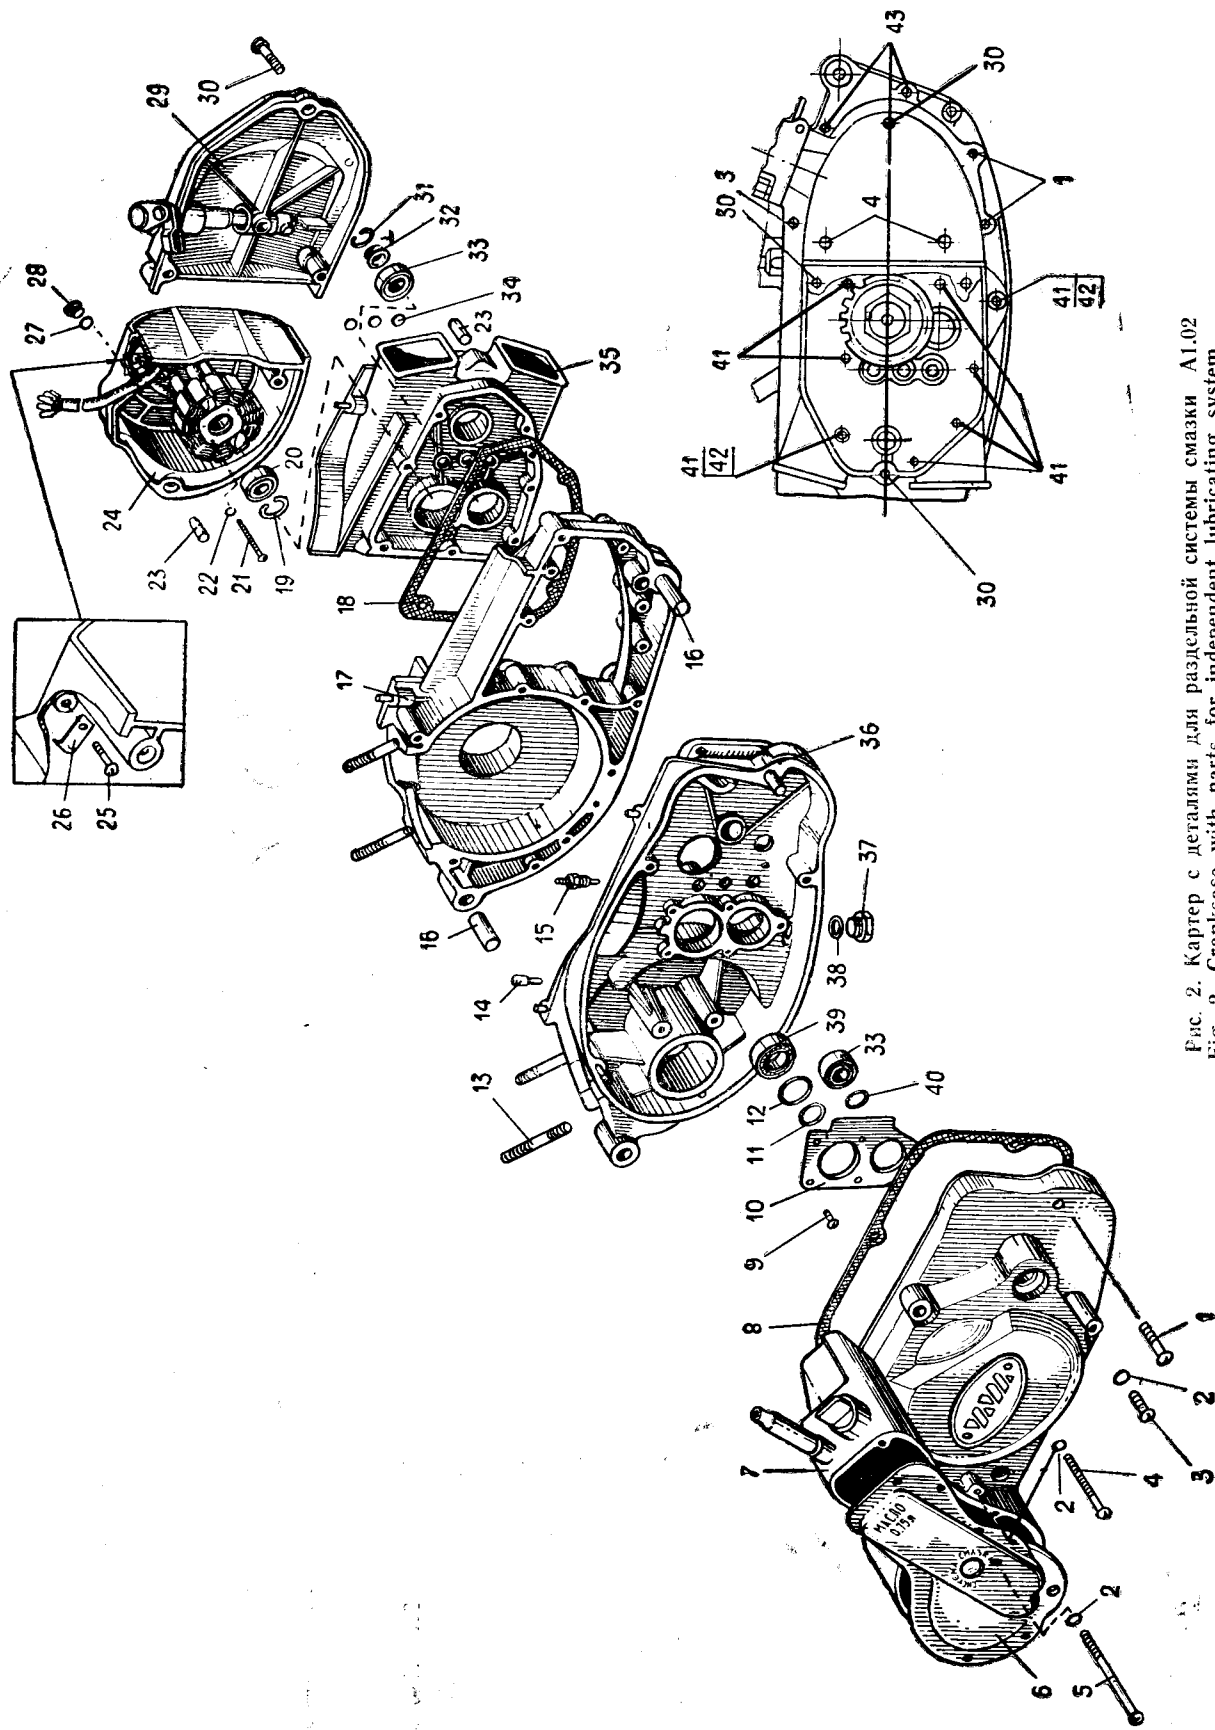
Картер с деталями для раздельной системы смазки А1.02
